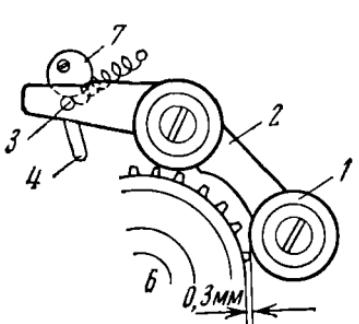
Каретка придерживающего ролика кинопроектора типа КН.
